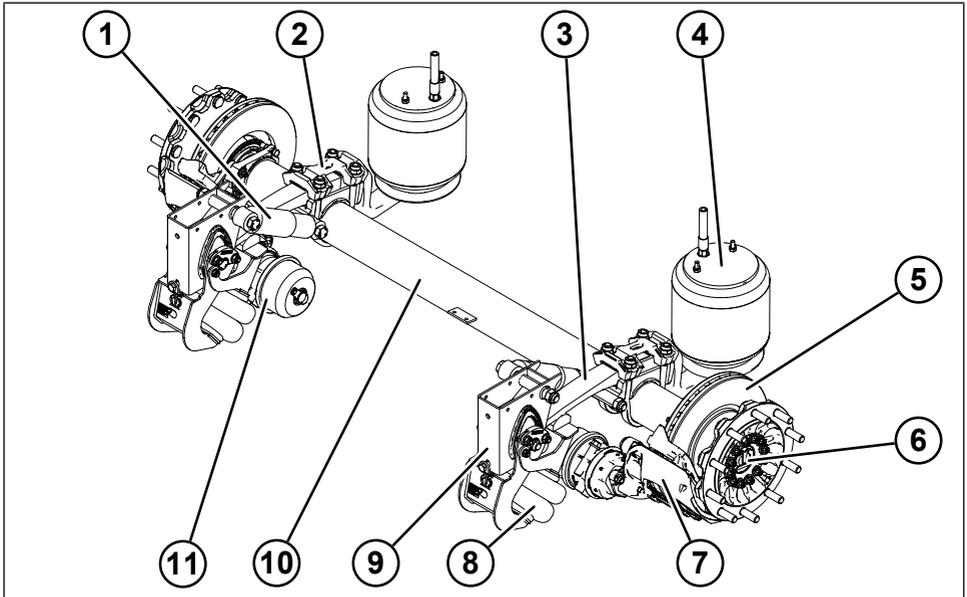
Übersicht KRONE Trailer Achse Scheibenbremse (Luftfederlenker oben)
